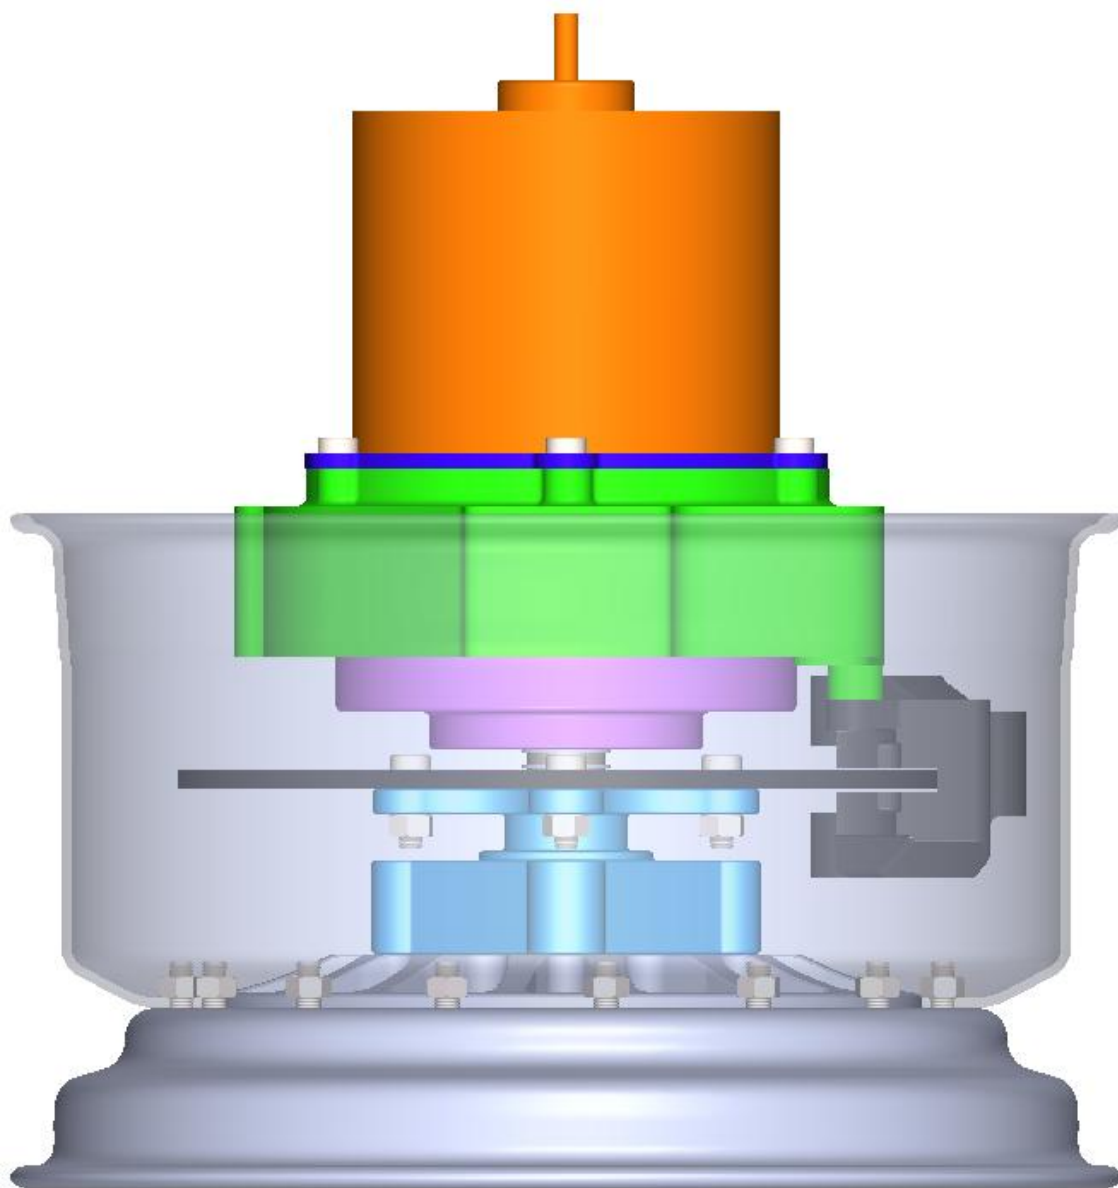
Vista superior del ensamble CAD 3D del sistema de transmisión IWM propuesto.
